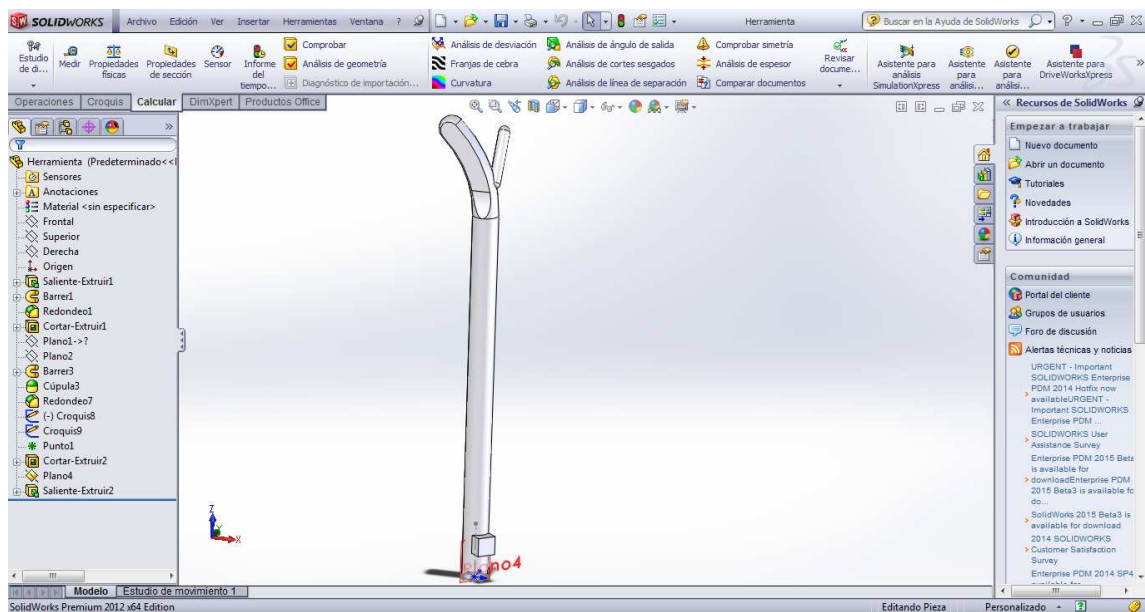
Vista 1 del conjunto parte metálica+acelerómetro en SOLIDWORKS
